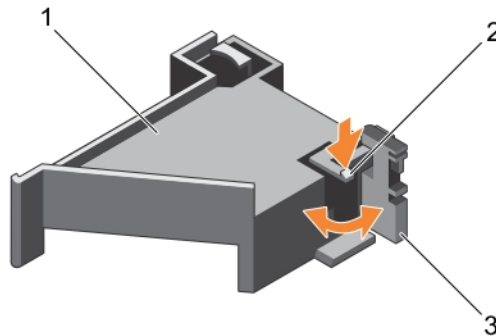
Ouverture et fermeture du loquet du support de carte PCIe
